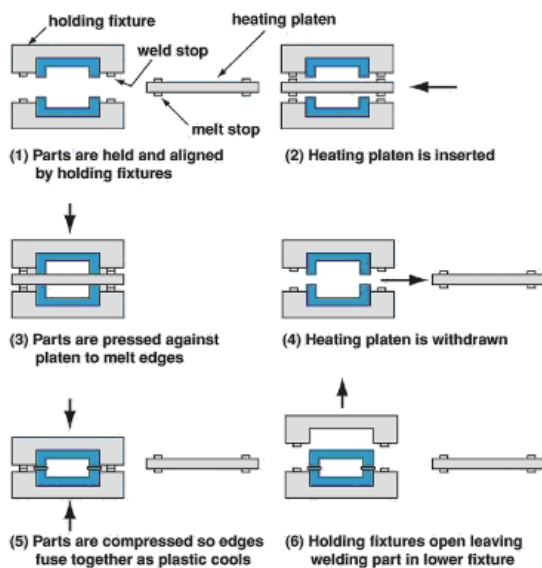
Rappresentazione schematica del processo "hot tool welding"
